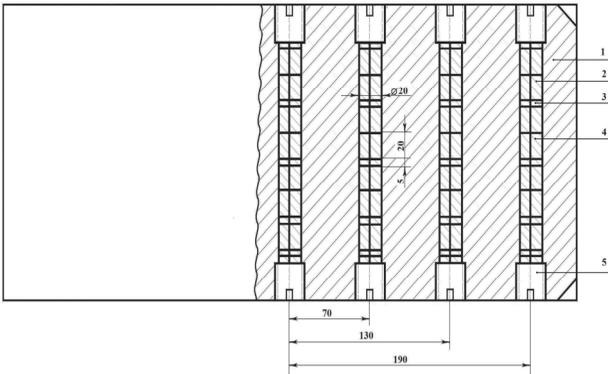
Конструкция монтажных стержней и их размещение в теле заготовки
